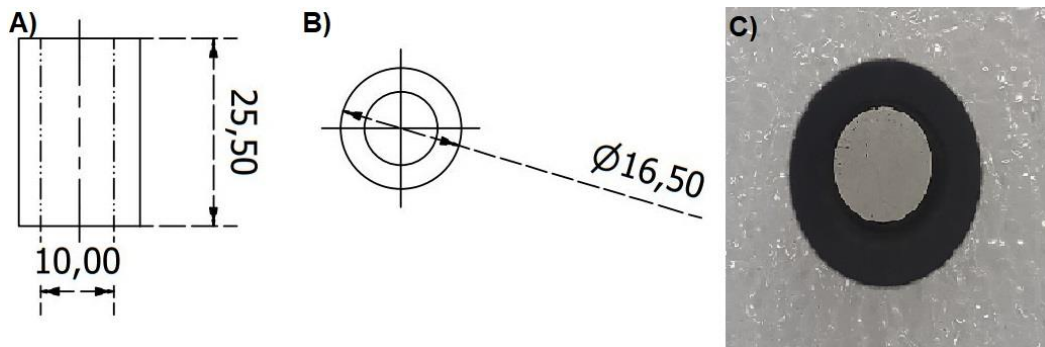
Espaciador. a) Plano vista lateral, b) Plano vista superior, c) Foto vista superior. Las dimensiones están en milímetros.
